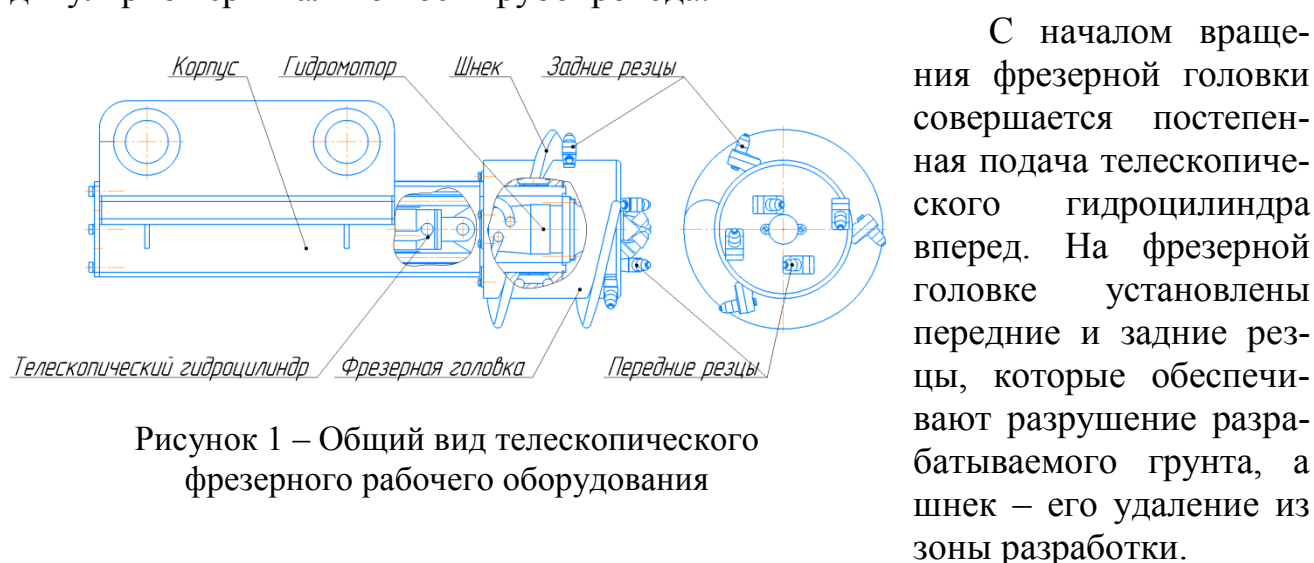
Общий вид телескопического фрезерного рабочего оборудования
